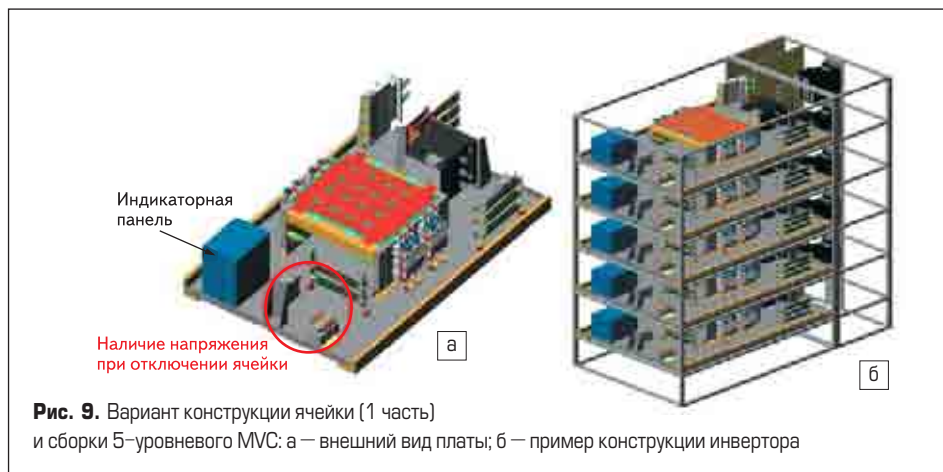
Вариант конструкции ячейки (1 часть) и сборки 5-уровневого MVC: а — внешний вид платы; б — пример конструкции инвертора
